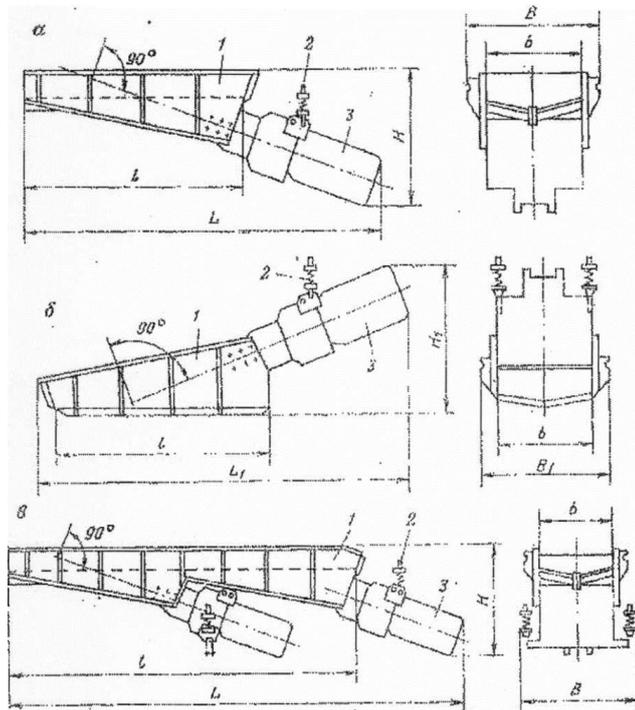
Вибрационный питатель ПЭВ-3: а - с нижним расположением вибратора; б - с верхним расположением вибратора; в - с нижним расположением двух вибраторов
